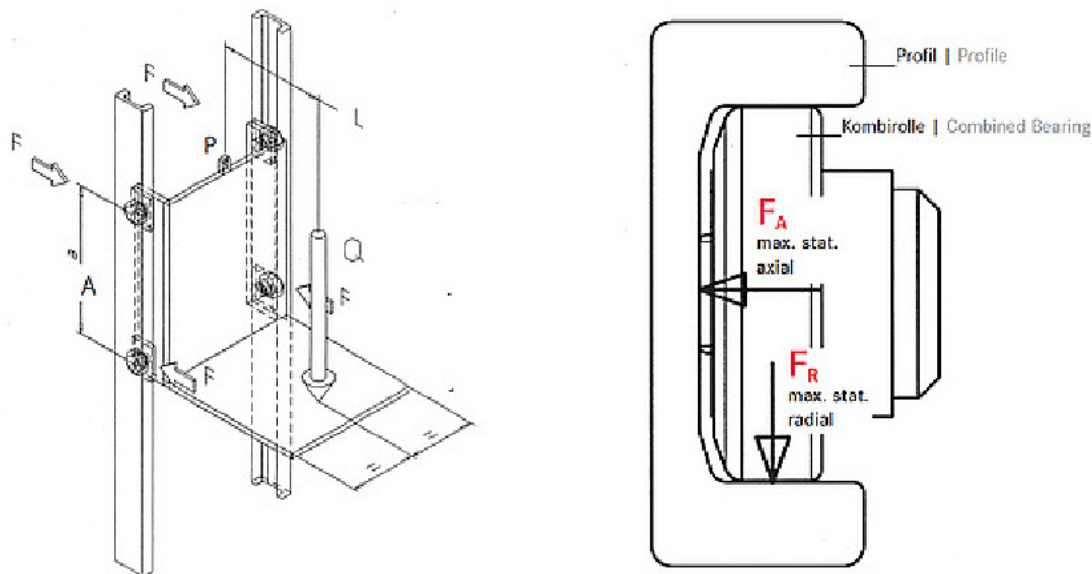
Skizze für die Rollenberechnung F. Winkel
